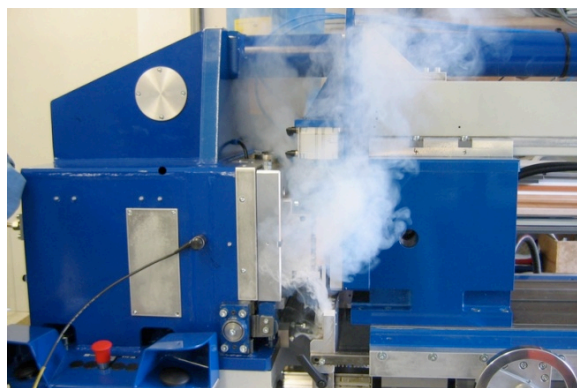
Prototype d'une machine conçu pour le soudage du bois à l'EPFL
